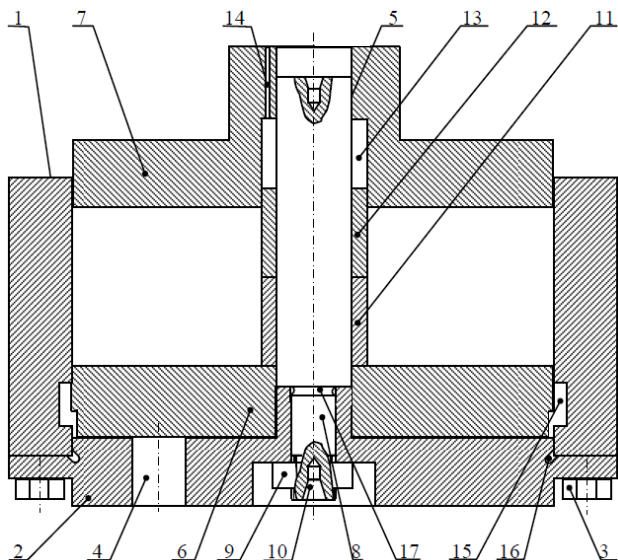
Пресс-форма для прессования шлифовального круга со втулкой:
